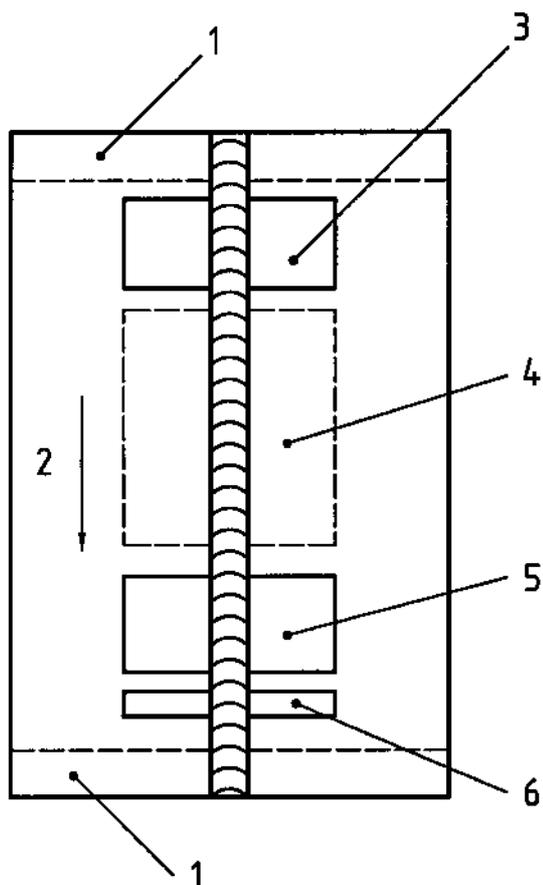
Расположение образцов для испытаний стыкового соединения при сварке пластин
